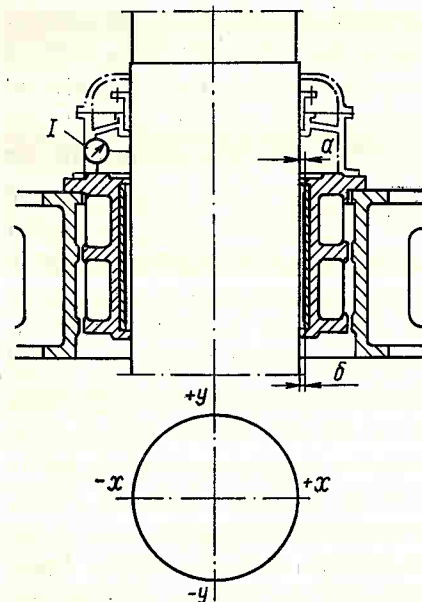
Формуляр на установку подшипника с обрезиненным вкладышем
